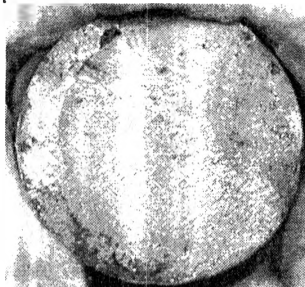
Поверхность усталостного излома образца из Стали 45 с покрытием из порошковой проволоки ПП-Нп-80Х20Р3Т
